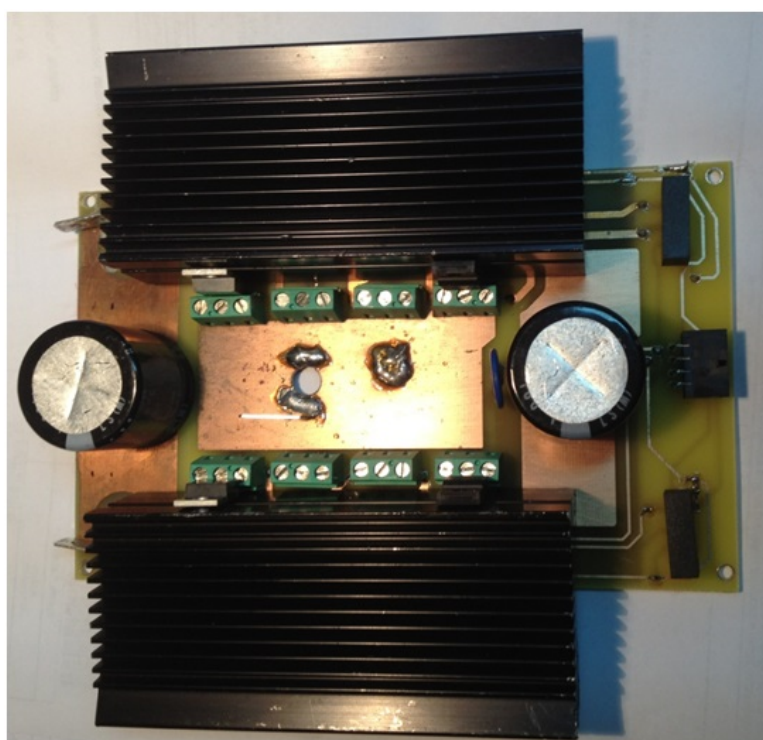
Aspecto final do braço da ponte H, depois de todos os componentes serem soldados
